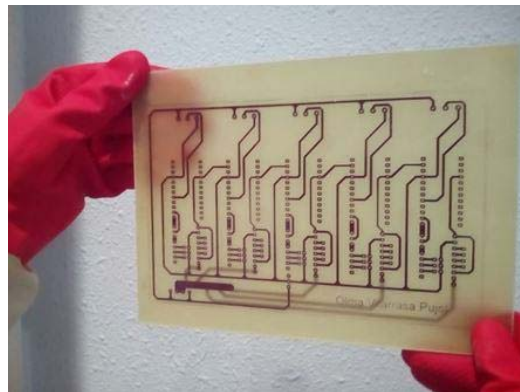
Placa PCB fotosensible de doble cara, on s'insereixen tots els components. Font: [319].
